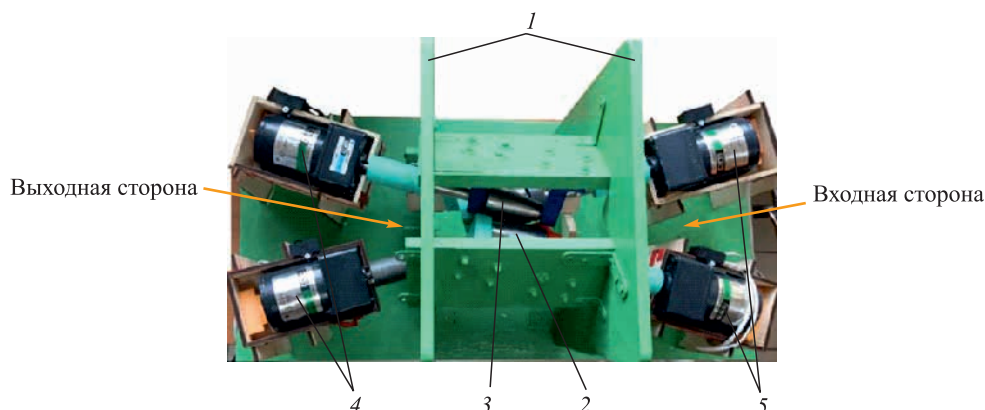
Макет четырехвалкового стана винтовой раскатки
